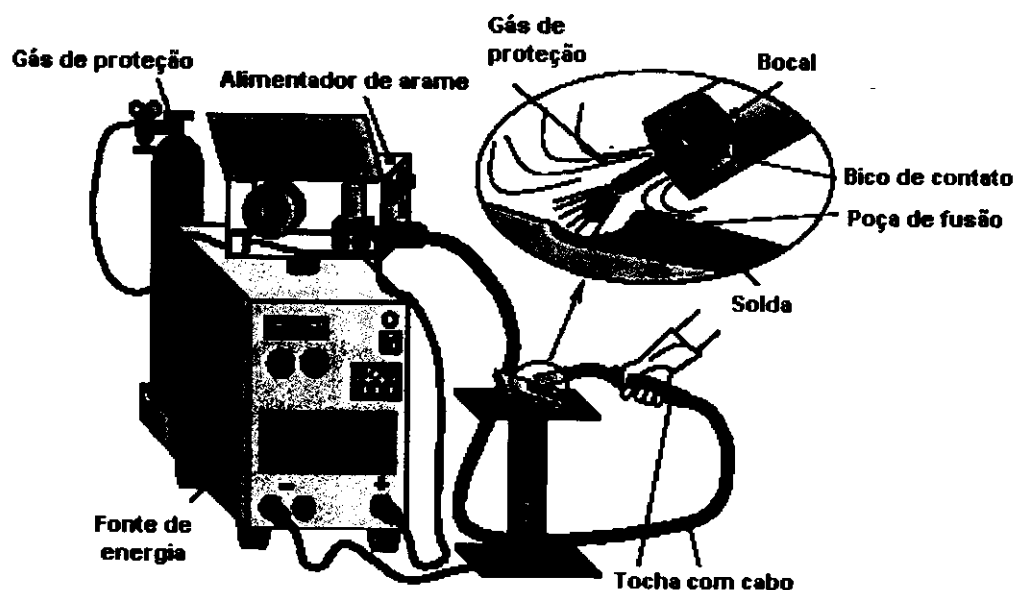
Equipamento para a soldagem MIG/MAG (Miranda, 2002).
